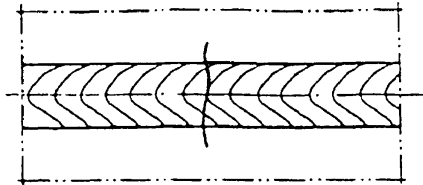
Поперечная трещина сварного соединения
